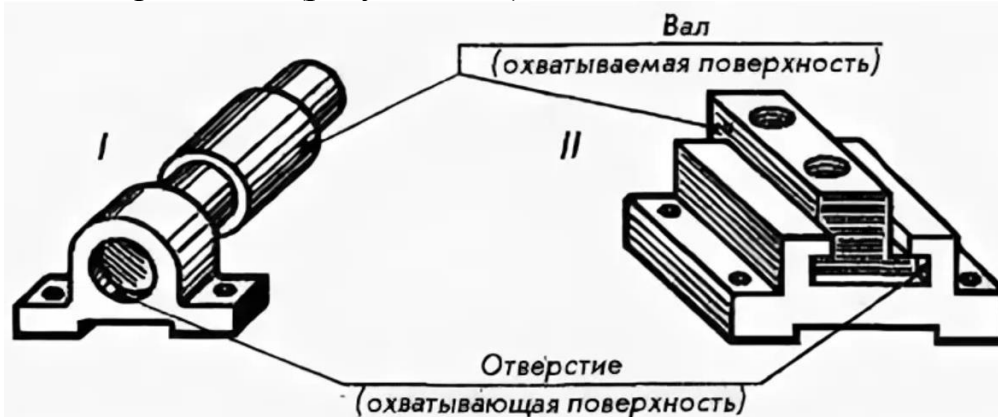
Охватываемая («Вал») и охватывающая («Отверстие») поверхности
